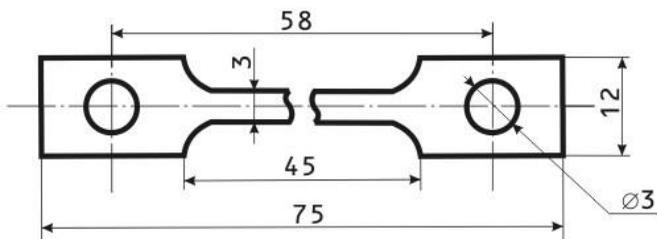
Форма и размеры образца для проведения испытаний на установке ИМАШ-20-75
